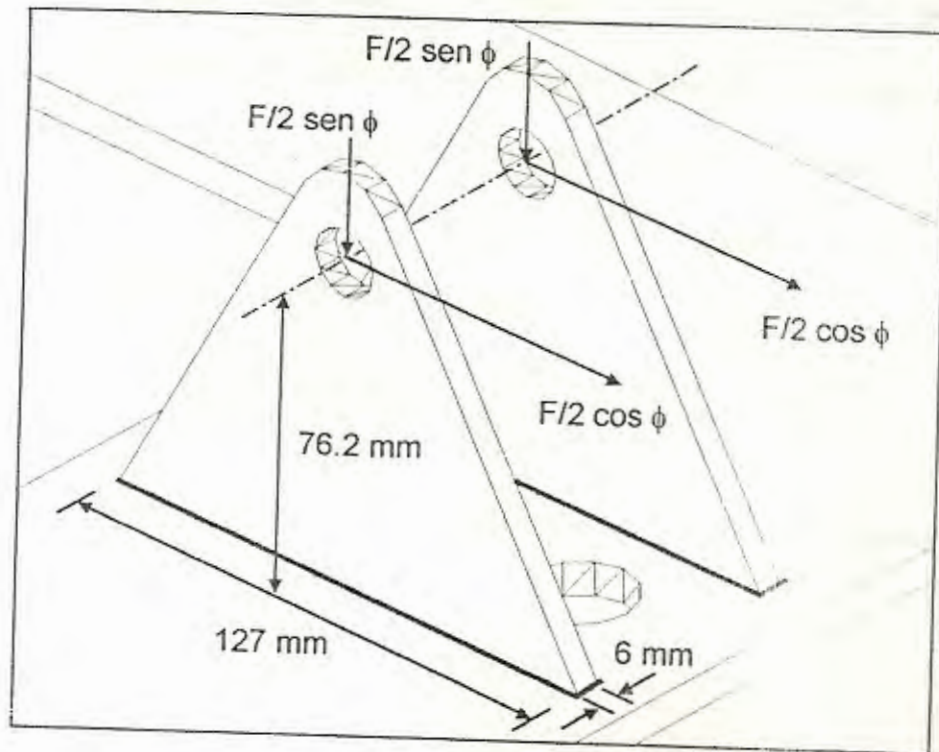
FUERZAS APLICADAS EN MENSULAS
